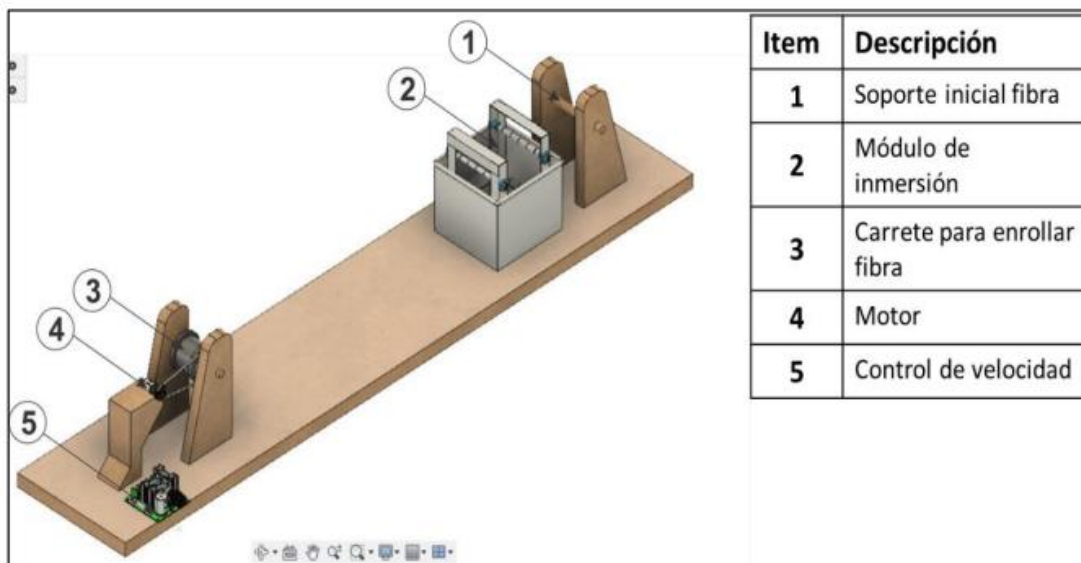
Diseño de sistema para realizar la técnica de inmersión [37].
